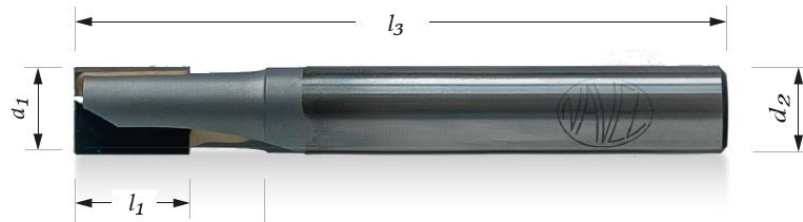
TK 2břítá fréza s kulovým čelem a upravenou geometrií
